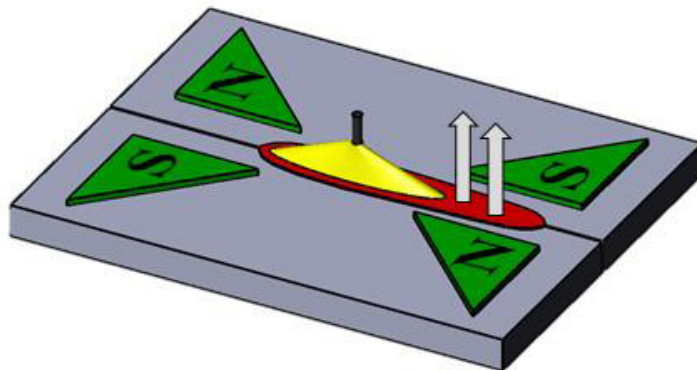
Схема удержания сварочной ванны четырёхполюсным магнитным полем при сварке на обратной полярности [Scheme of holding the welding bath with a four-pole magnetic field when welding on the reverse polarity]
